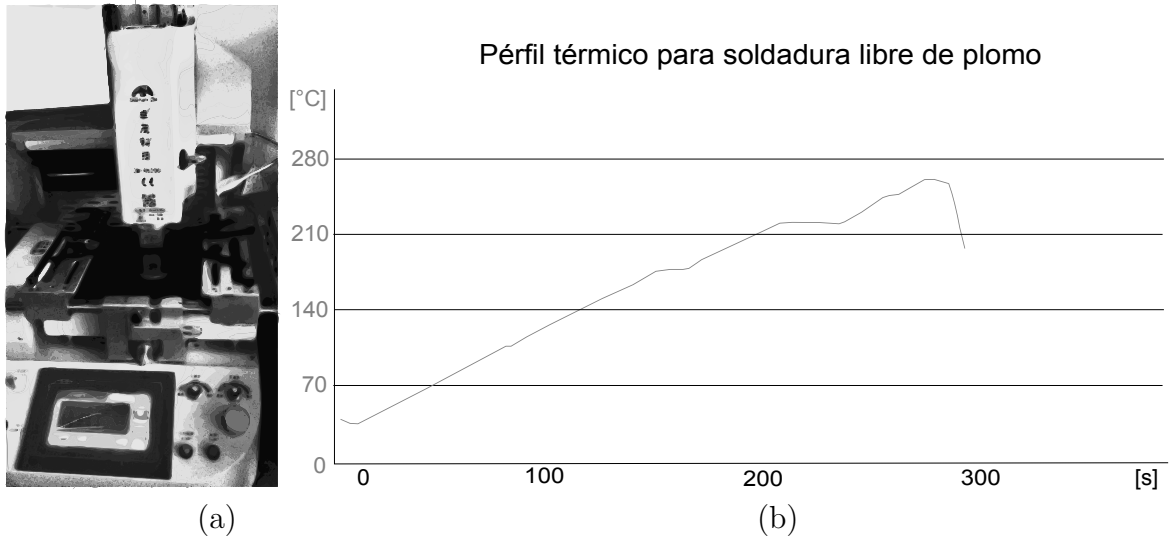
Equipo de soldado (a) y perfil térmico utilizado en el soldado del dispositivo MPU-9150 (b).
